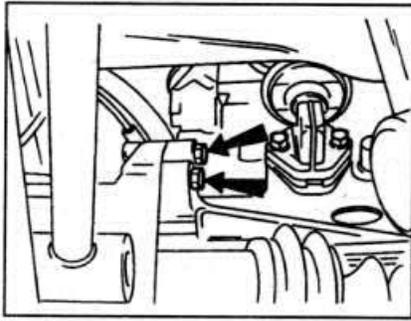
D.7. Болты крепления выступа коробки передач к двигателю.
